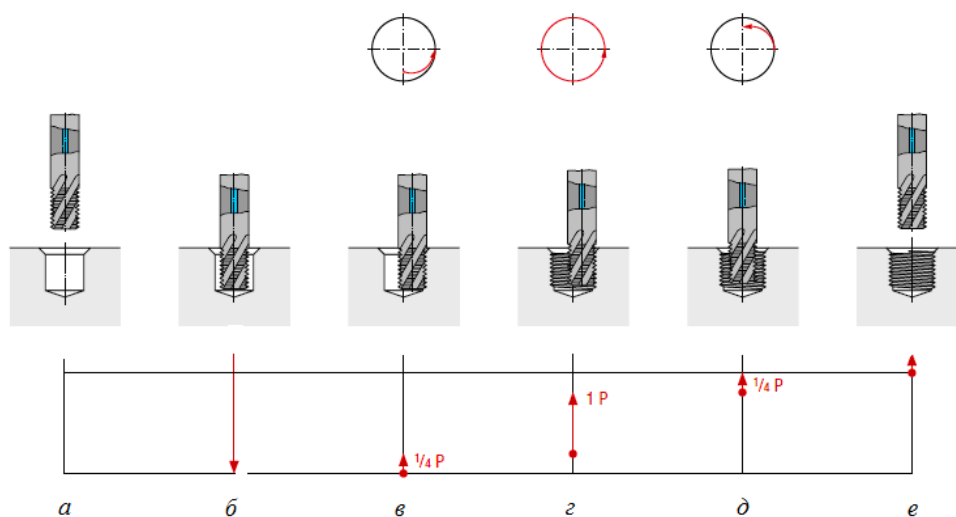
Кинематическая схема работы гребенчатой резьбовой фрезой [7]
